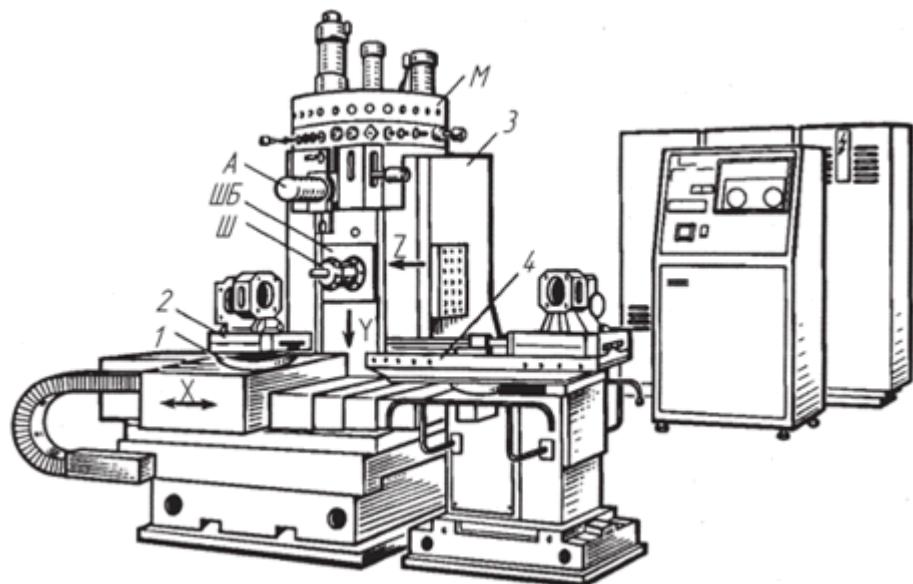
Загальний вигляд БЦ з горизонтальною віссю обертання шпинделя
